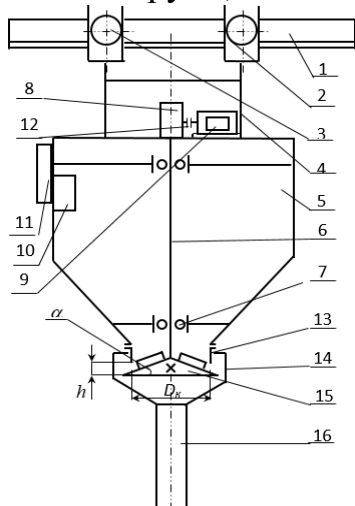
Схема автоматизованого індивідуального роздавача-дозатора сипких кормів: 1 – нерухома балка; 2 – рухомі каретки; 3 – електродвигун приводу кареток; 4 – рама; 5 – бункер роздавача-дозатора; 6 – привідний вал; 7 – підшипники; 8 – електродвигун з редуктором приводу робочого органу; 9 – вимірювач частоти обертання; 10 – мікропроцесорний блок управління; 11 – блок живлення; 12 – муфта; 13 – насадка випускної горловини бункера; 14 – захисний кожух; 15 – конусно-лопатевий робочий орган; 16 – напрямляч потоку.
